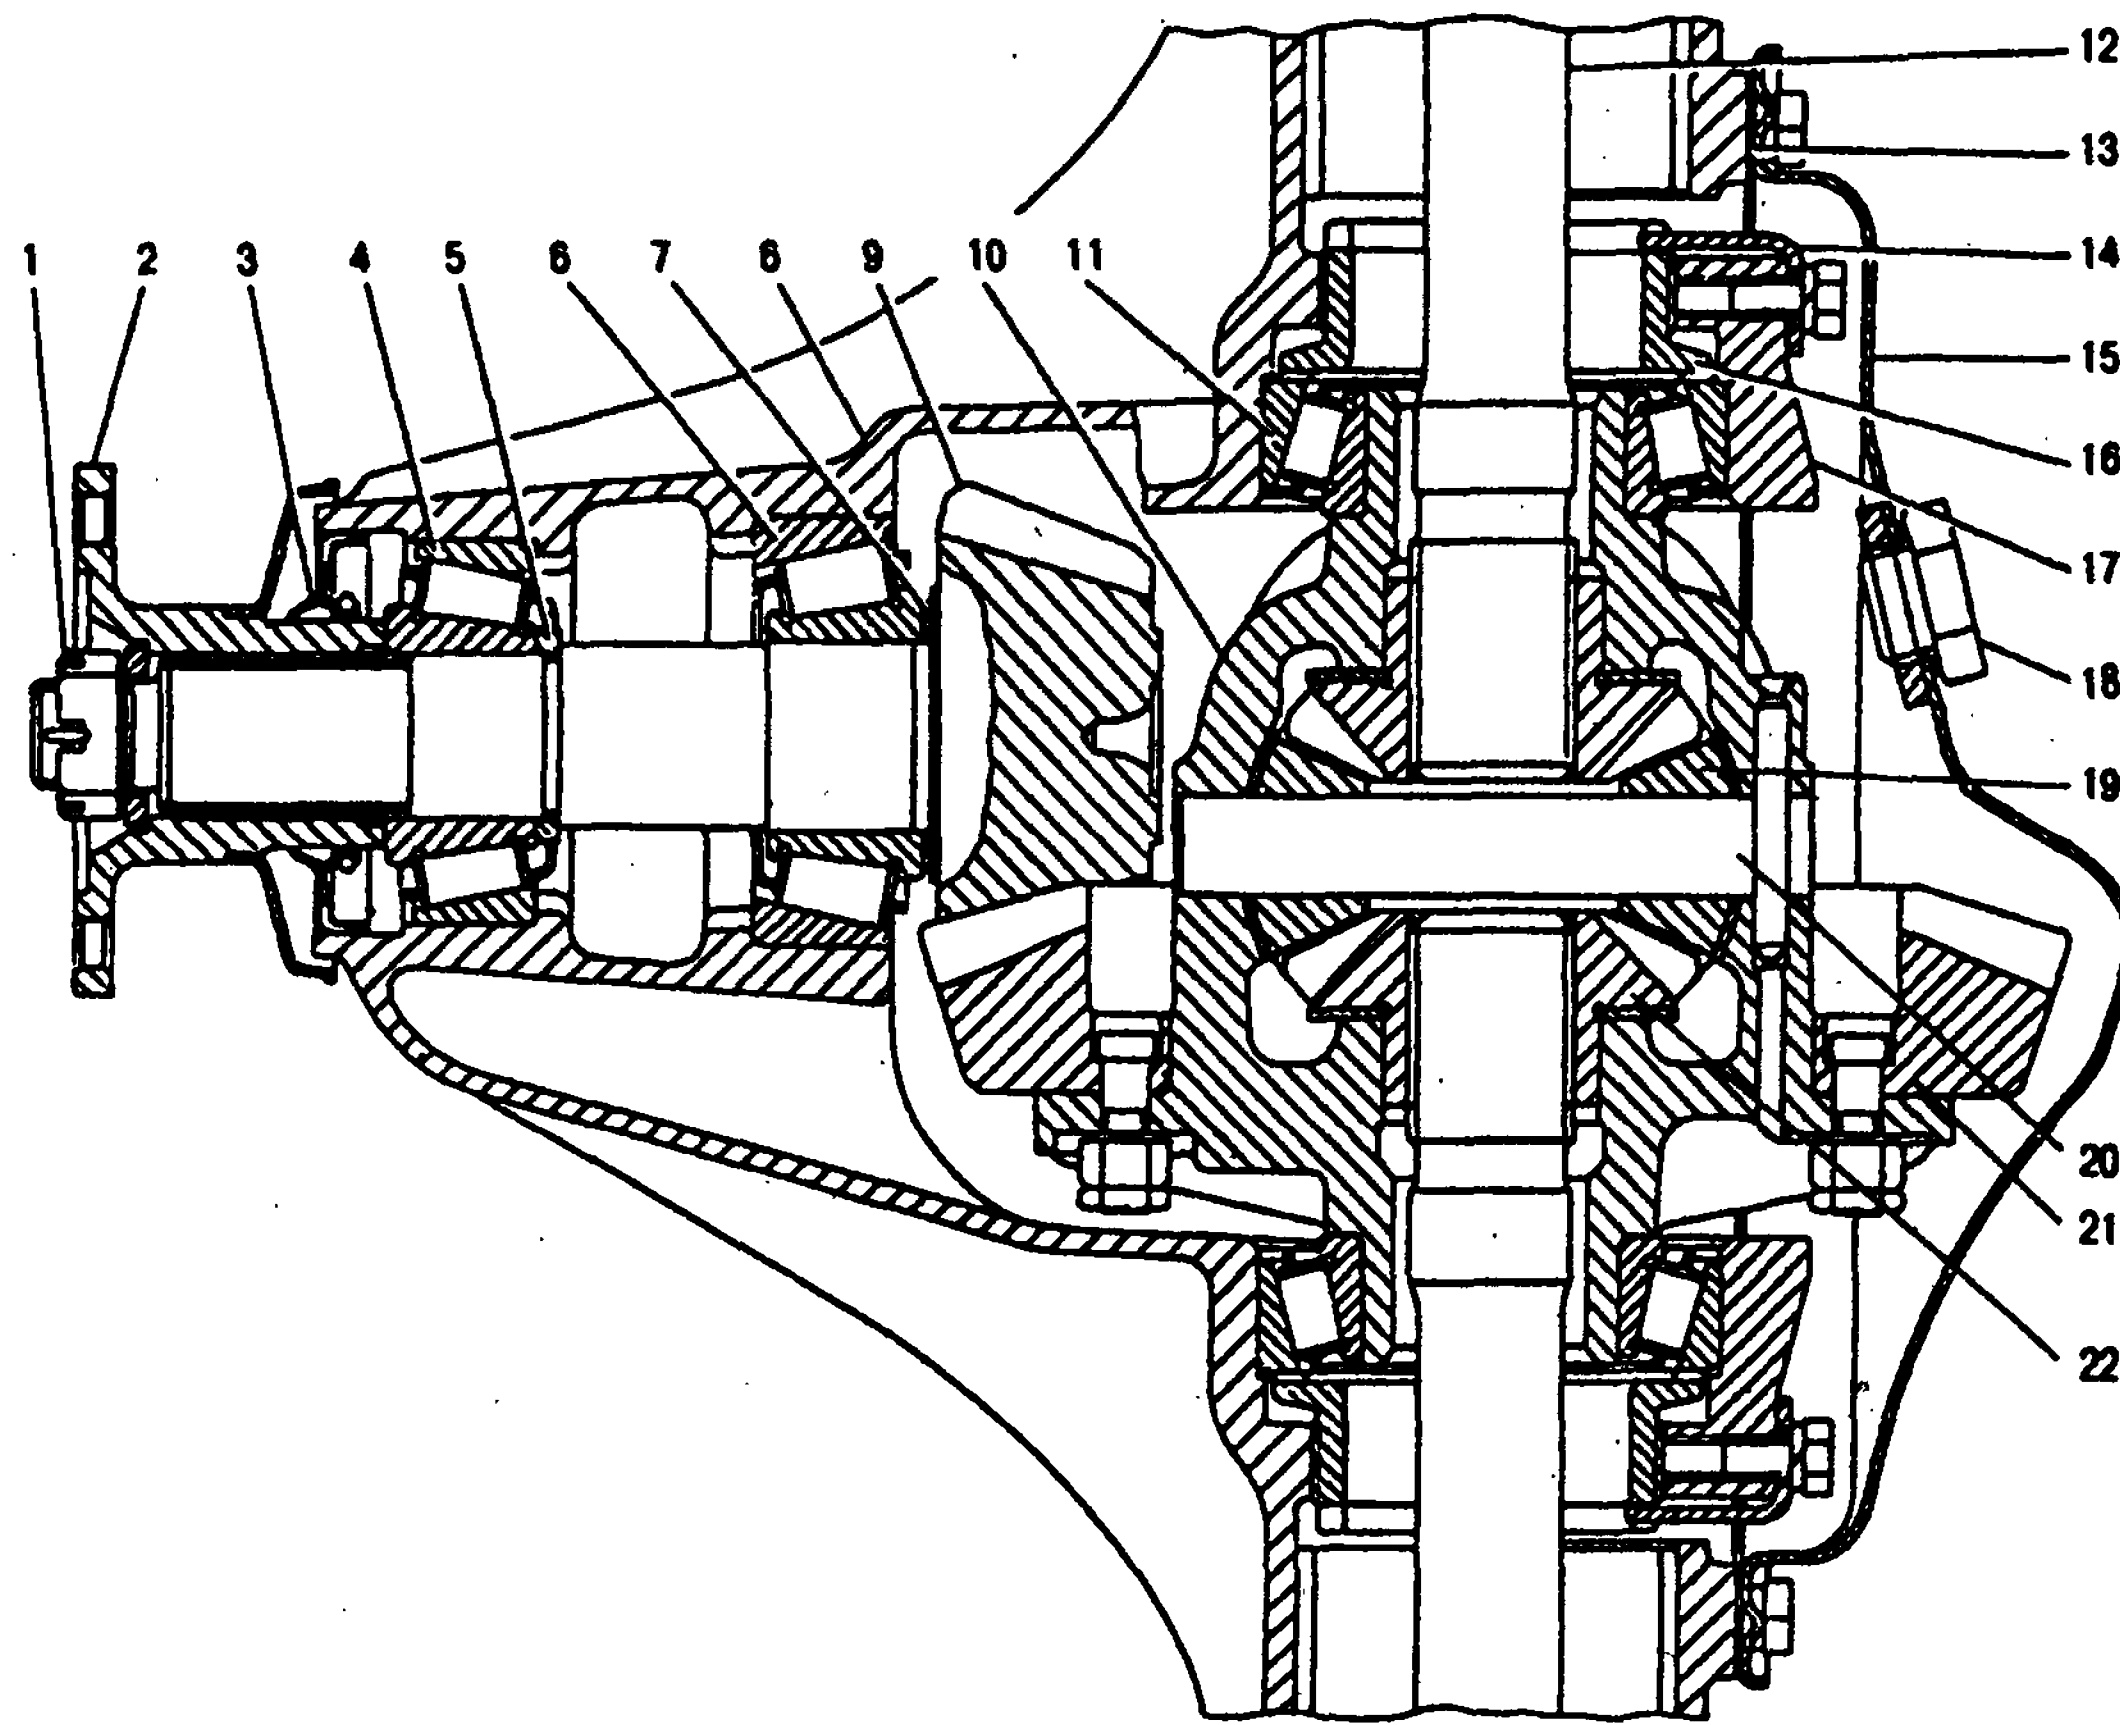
Задний мост (средняя часть): 1 - гайка; 2 - флажки ведущей шестерни; 3 - манжета; 4 - подшипник ведущей шестерни передний; 5 - регулировочная шайба; 6 - подшипник ведущей шестерни задний; 7 - регулировочное кольцо; 8 - картер; 9 - ведущая шестерня; 10 - корпус дифференциала; 11 - подшипник дифференциала; 12 - полуось; 13 - прокладка крышки; 14 - стопорная пластина; 15 - крышка картера; 16 - регулировочная гайка подшипника дифференциала; 17 - крышка подшипника дифференциала; 18 - пробка; 19 - сателлит; 20 - ось сателлитов; 21 - ведомая шестерня; 22 - полуосевая шестерня
